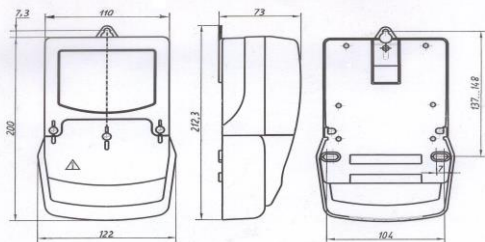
Загальний вигляд лічильника CE102-U в корпусі S7
